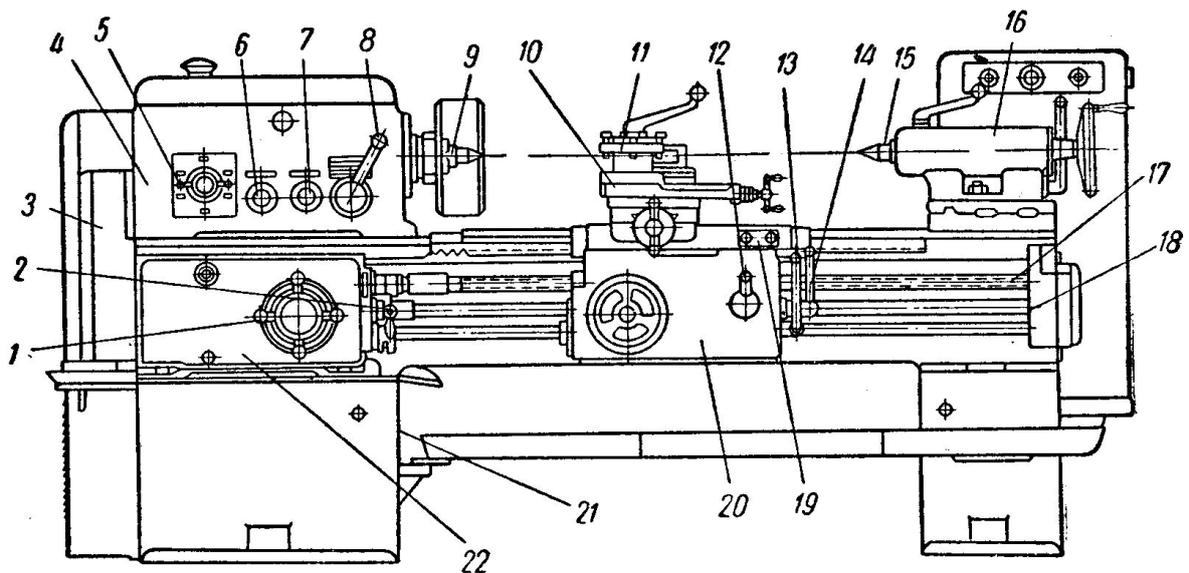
Схема токарно-винторезного станка 1К62: 1 – рукоятка переключения скорости передач; 2 – рукоятка включения шпинделя; 3 – привод; 4 – передняя бабка; 5 – рукоятка регулировки чисел оборотов; 6 – рукоятка изменения подачи; 7 – рукоятка увеличения шага; 8 – рукоятка изменения чисел оборотов; 9 – центр шпинделя; 10 – суппорт; 11 – резцедержатель; 12 – рукоятка включения продольной подачи; 13 – рукоятка включения шпинделя; 14 – рукоятка реверсирования подачи; 15 – центр задней бабки; 16 – пиноль задней бабки; 17 – ходовой винт; 18 – ходовой вал; 19 – кнопка пуска и остановки главного двигателя; 20 – фартук; 21 – станина; 22 – коробка подач
